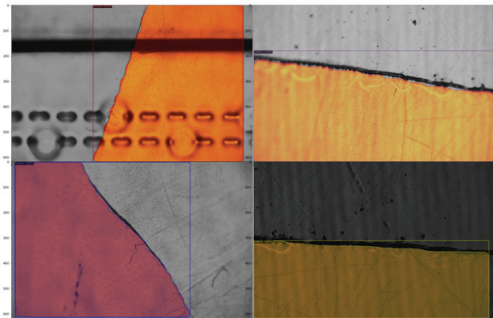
딥러닝을 이용한 PCB 기판 미박리 필름 검출 결과
